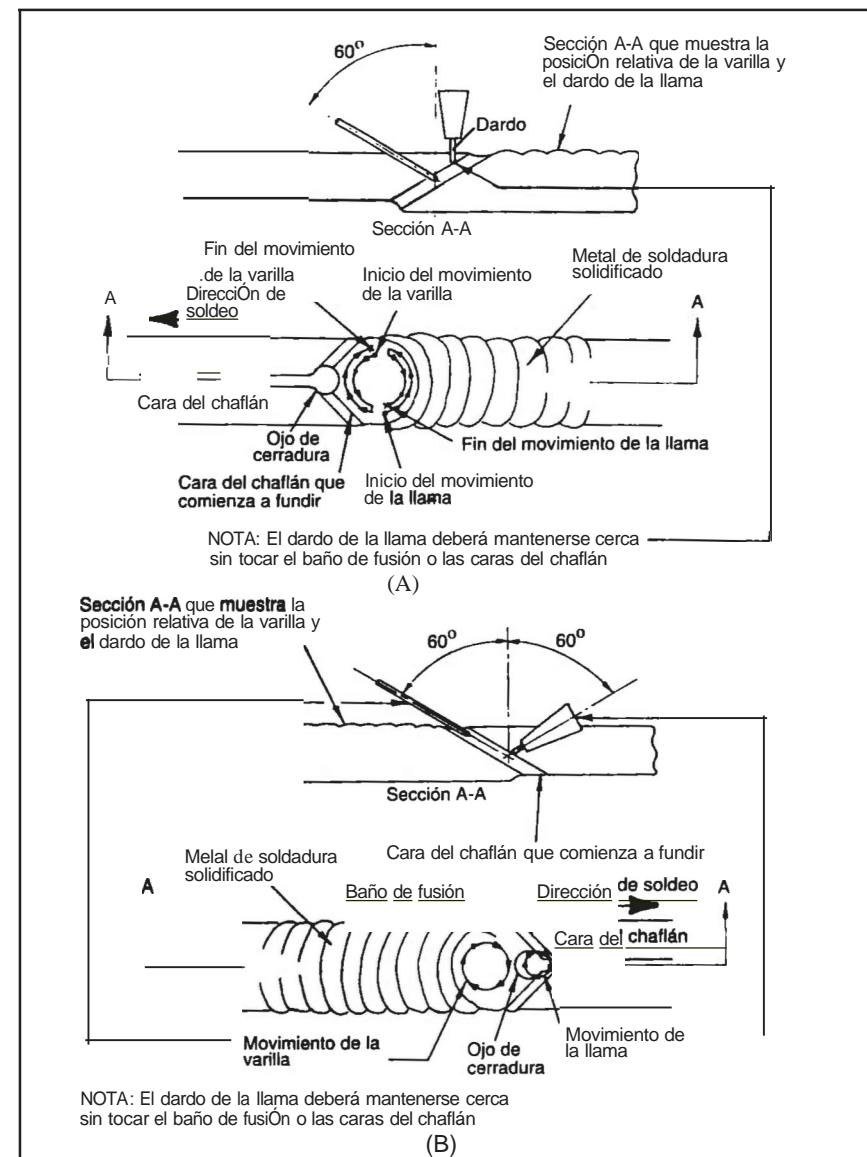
(A) T \acute{E} CNICA DE SOLDEO HACIA ADELANTE O A IZQUIERDAS.
